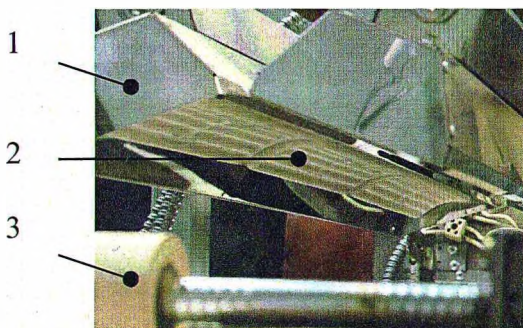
Камера предварительного нагрева прокатного станка по уплотнению шпона: 1 – защитный экран, 2 – инфракрасные лампы, 3 – резиновый валец для подачи неуплотненного шпона
